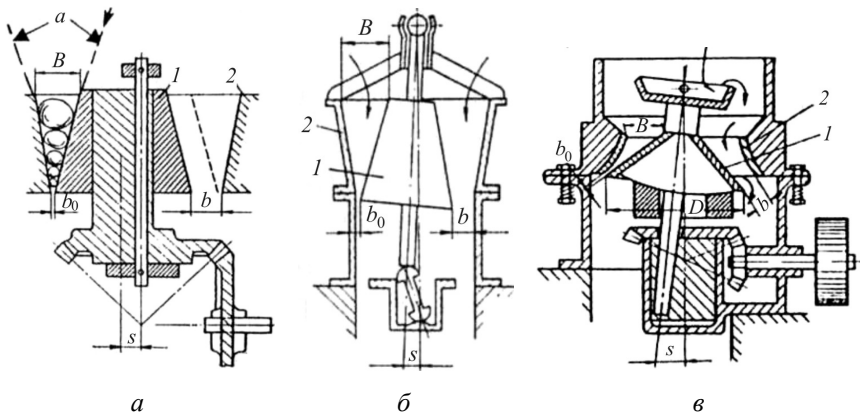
Принцип действия общий вид конусной дробилки: *а* – конусная дробилка с неподвижной осью (ККД); *б* – то же, с подвесным валом (ККД «гирационная»); *в* – то же, с консольным валом, опирающимся на шаровой подпятник (КСД и КМД); 1 – подвижный конус; 2 – неподвижный конус (корпус); *B* – ширина приемного отверстия; *b* – ширина разгрузочного отверстия; *a* – угол захвата
